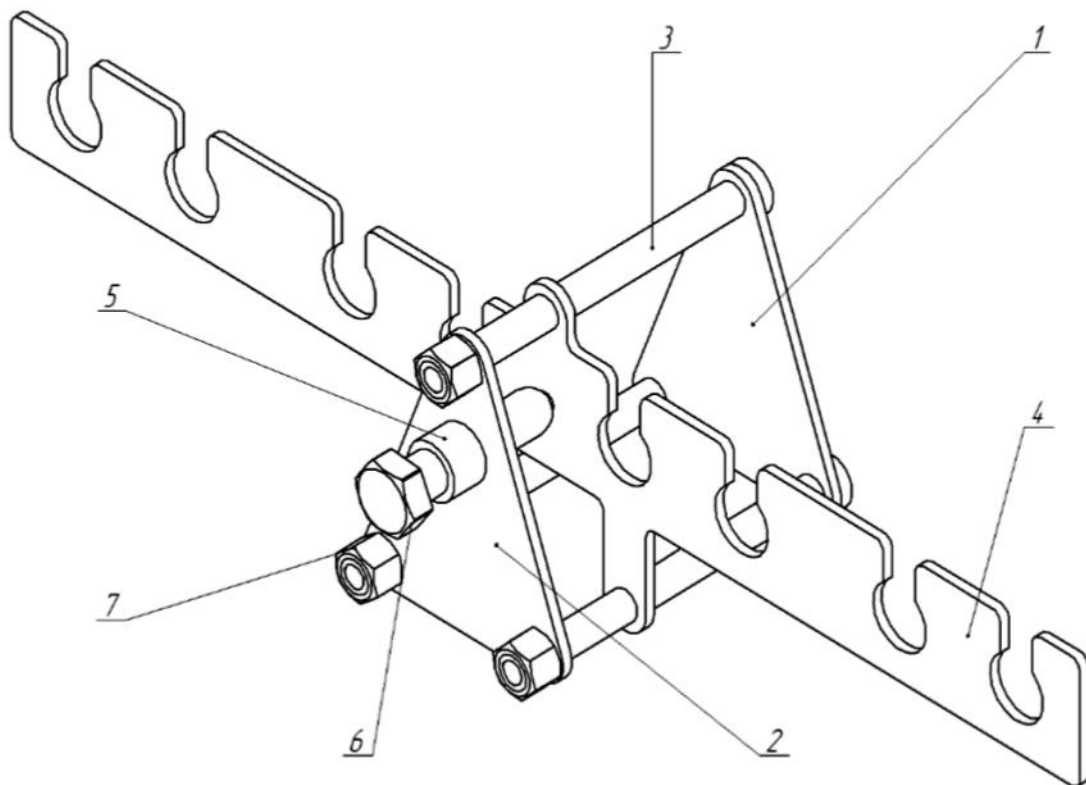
Пристрій для одночасного стискання клапанних пружин.
